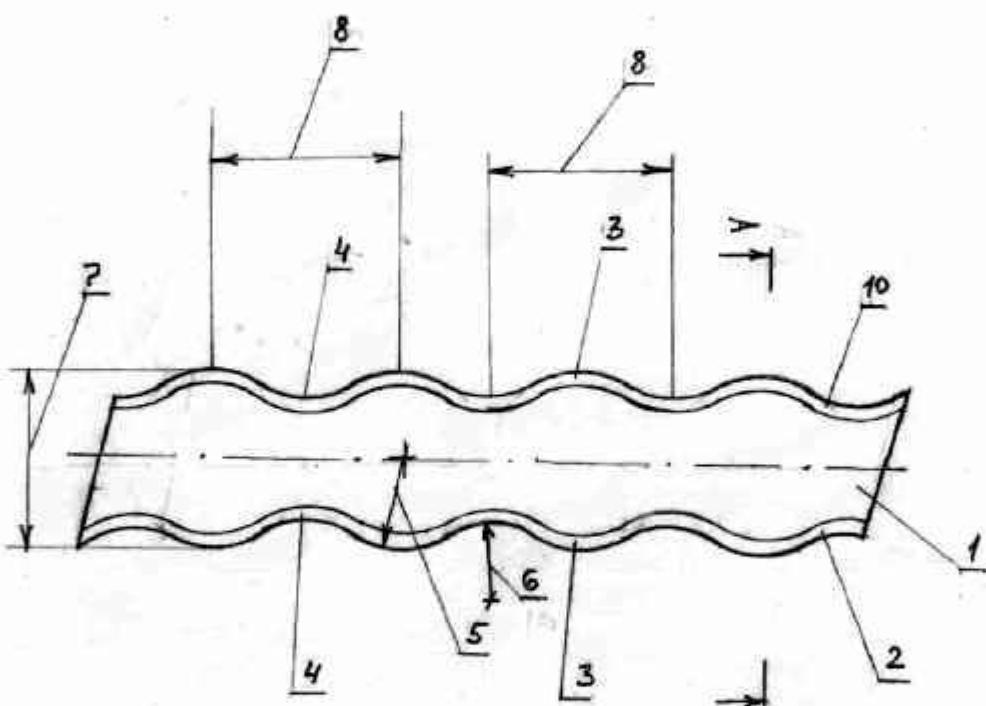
Двухсторонний зубчаторий нож плоскорезной лапы.
